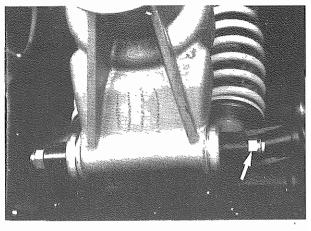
Dadi fissaggio portamozzo Hub holder nuts
